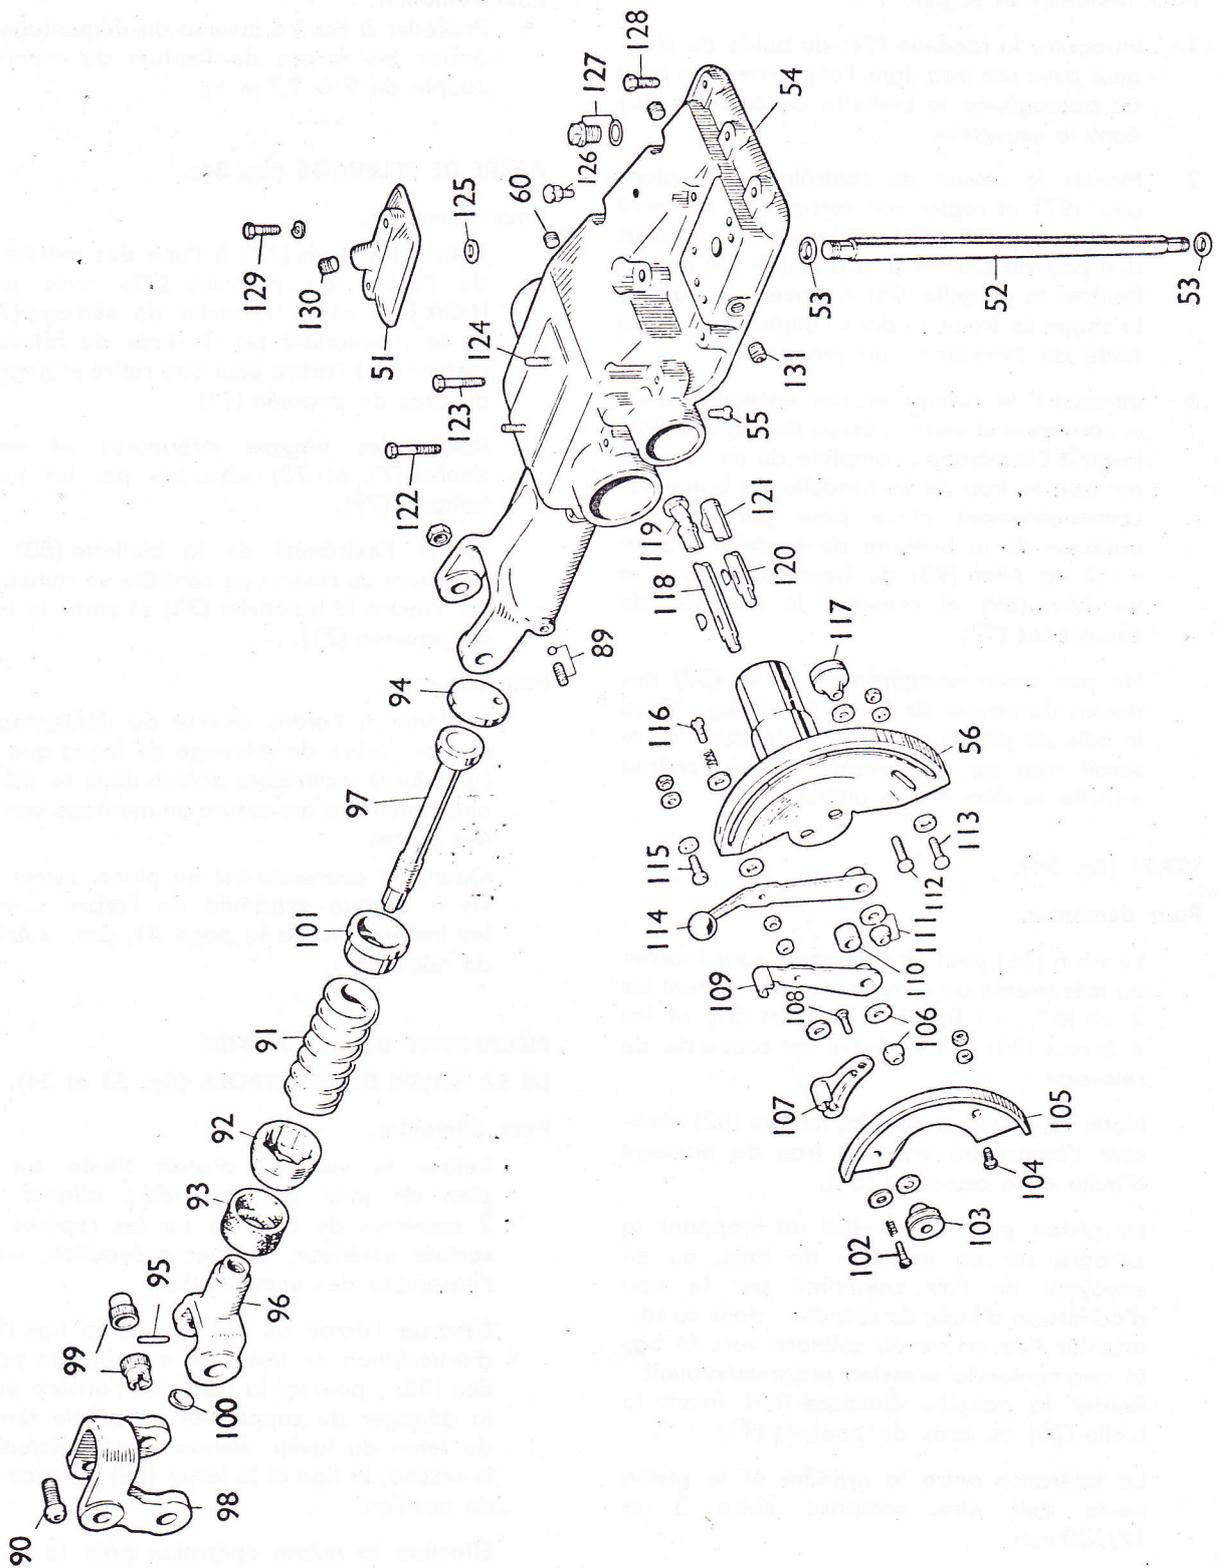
VUE ÉCLATÉE DU COUVERCLE DE RELEVAGE.
